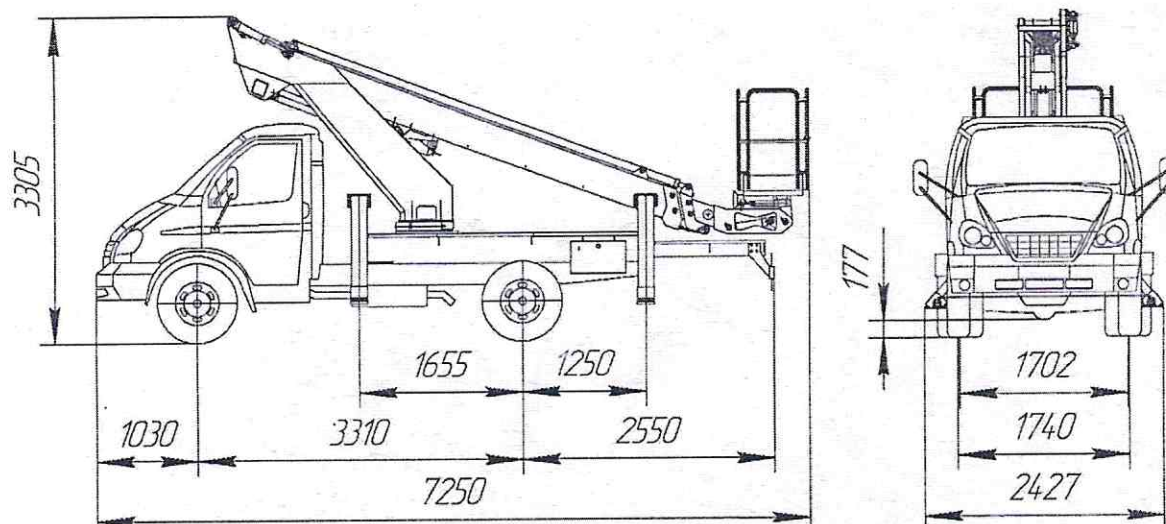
Габаритные размеры подъемника ВИПО-18-01
